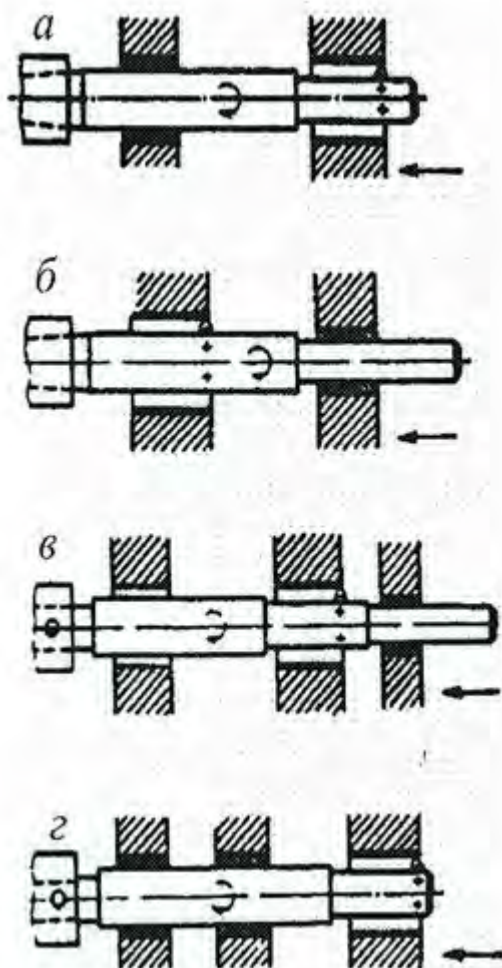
Схеми направлення інструмента кондукторними втулками
